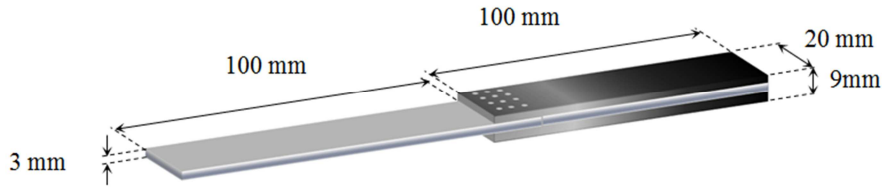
Géométrie de l'éprouvette double recouvrement (EDR)
